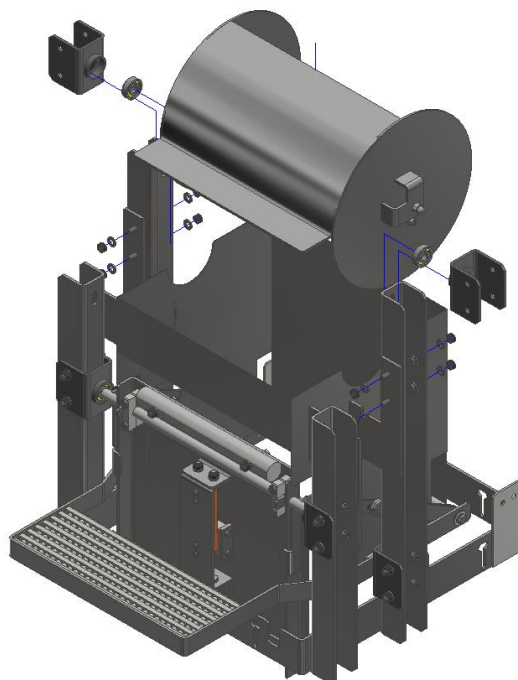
Spojení horních částí táhel se spodními částmi a jejich uchycení k desce
